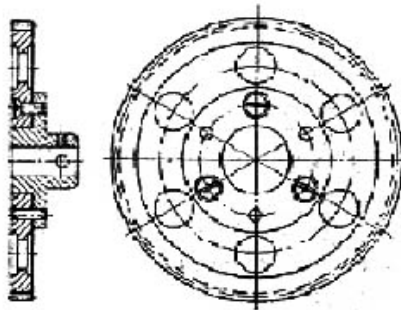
Зубчатое колесо сборной конструкции
